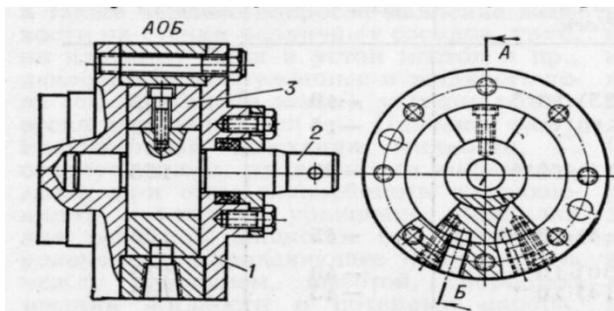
Моментный гидроцилиндр: 1 – корпус; 2 – вал; 3 – лопасть
